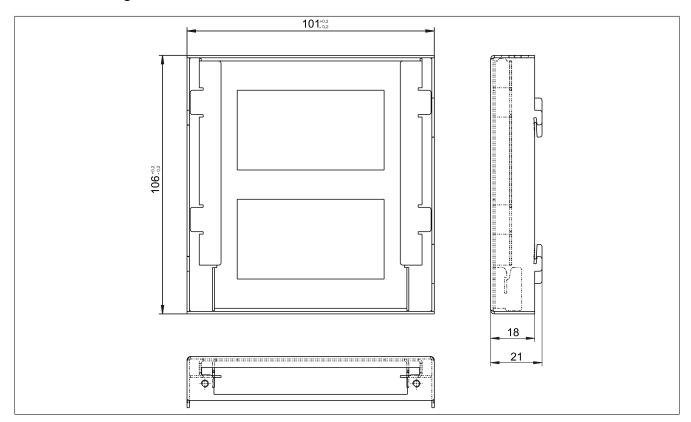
5AC801.FRAM-00 - Abmessungen
